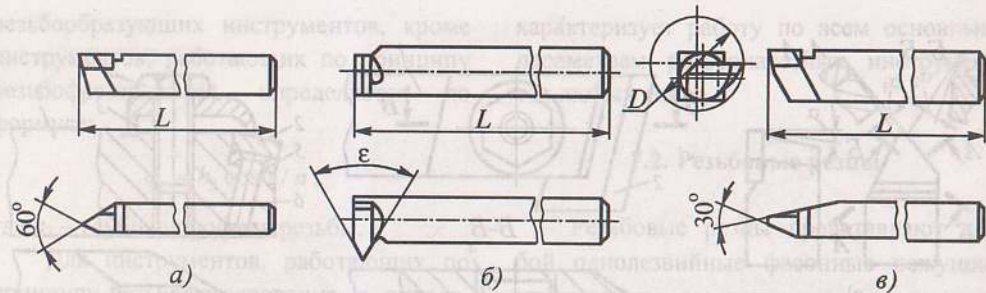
Виды резцовых резцов по типу нарезаемой резьбы
